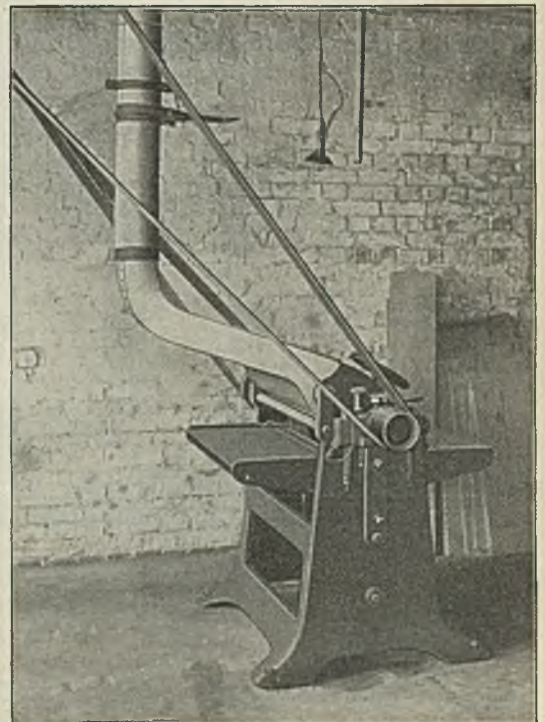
Späneabsaugung an einer Holz-hobelmaschine.
